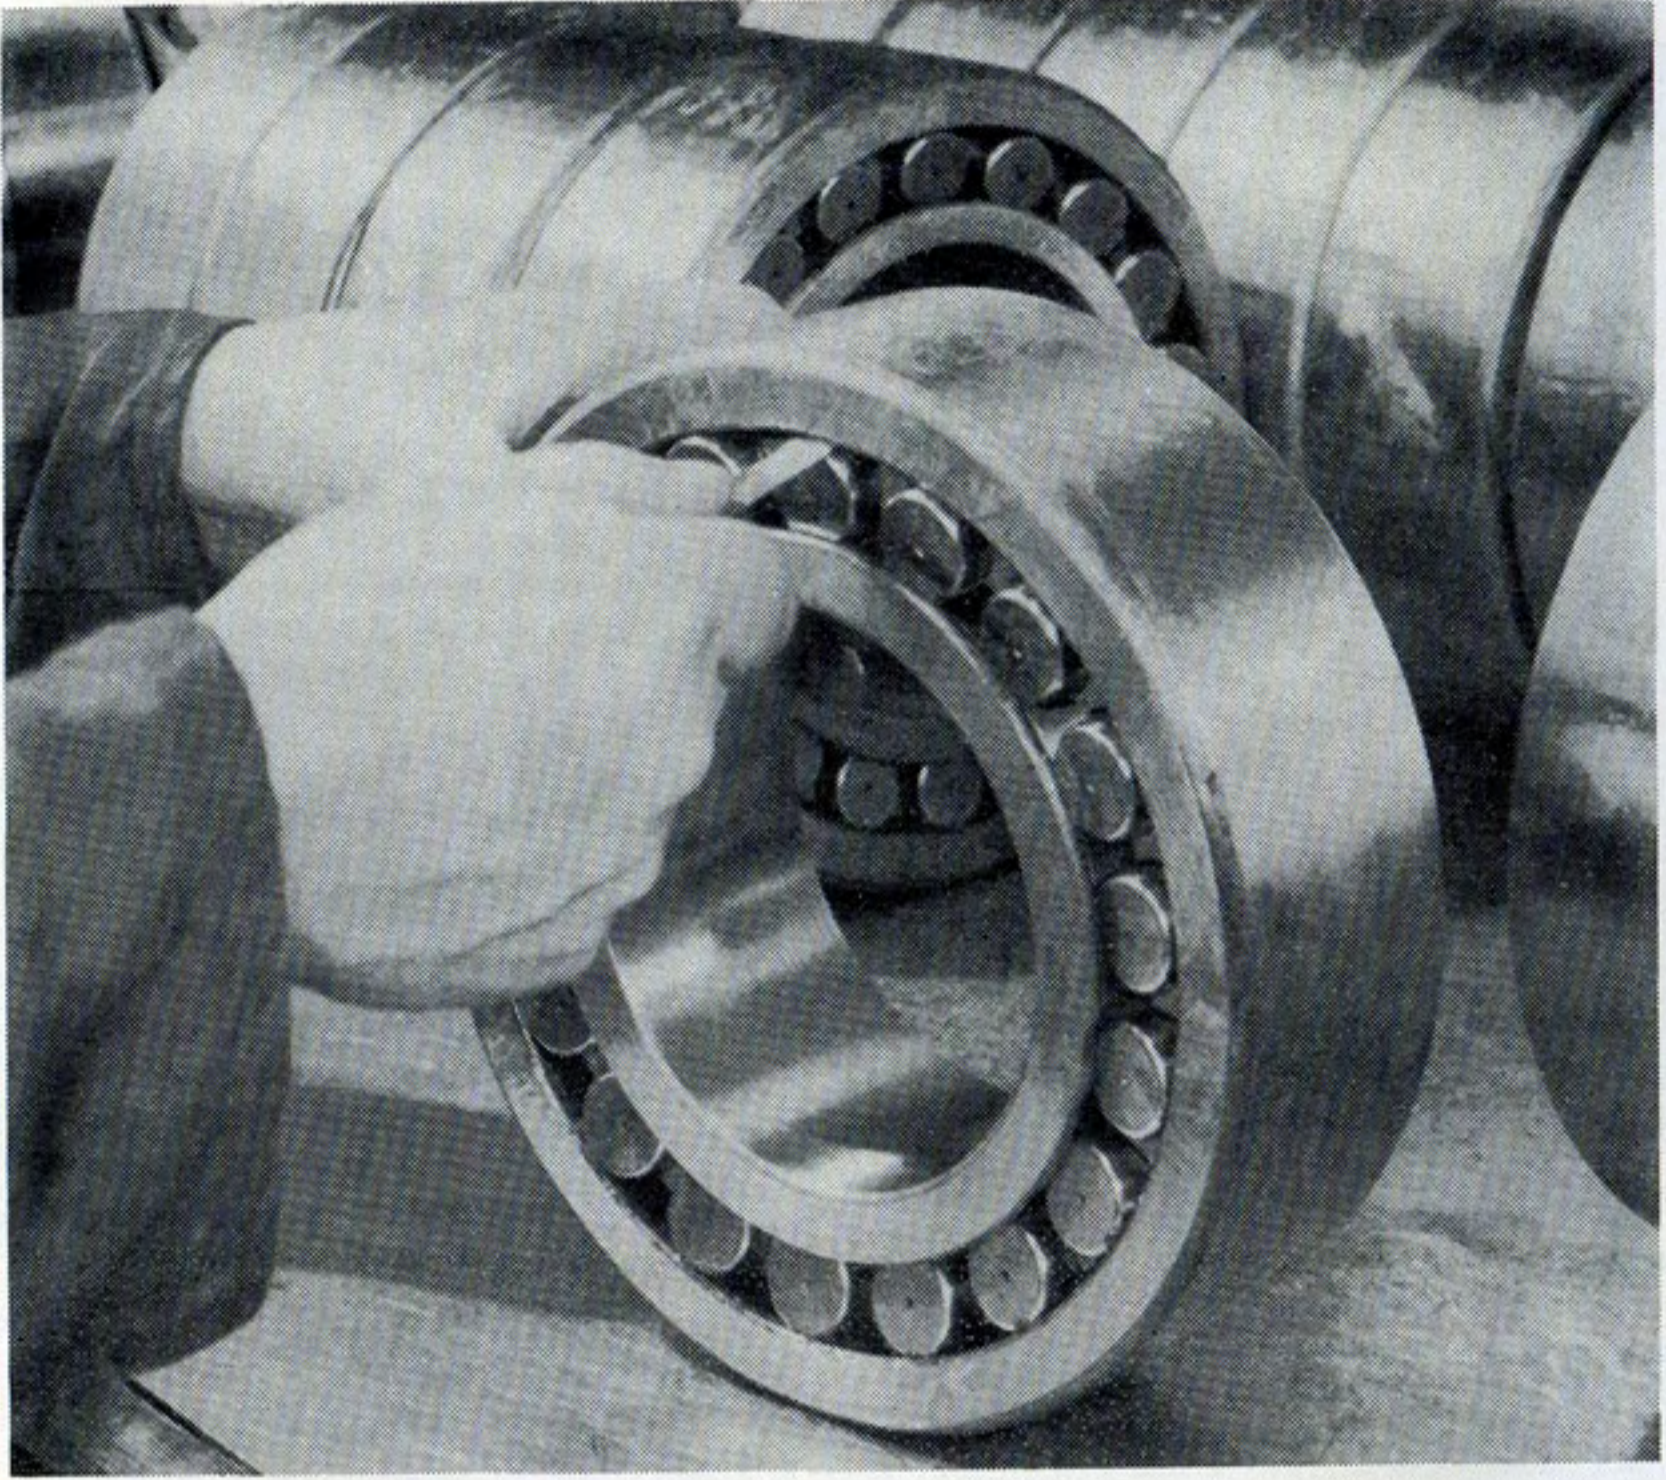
Mesure du jeu du roulement avant montage à l'aide de lames calibrées.
